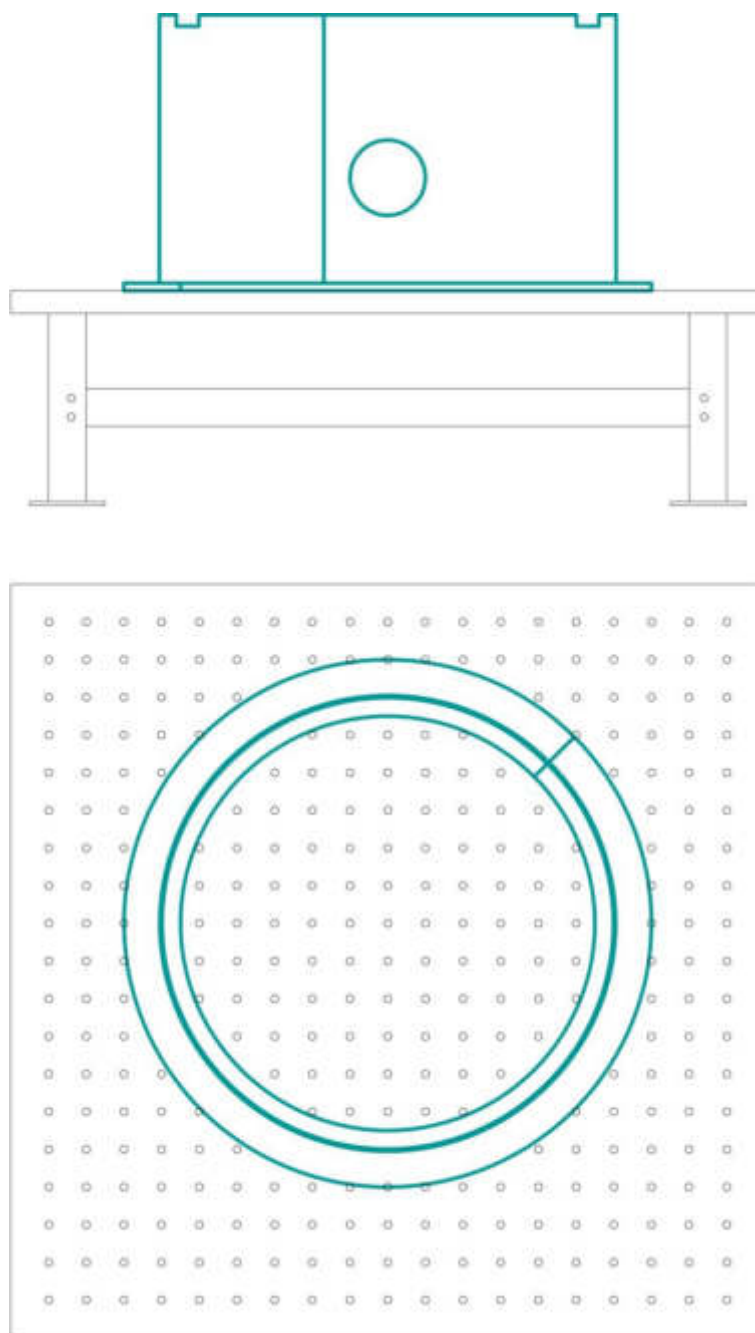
Схема сборки обечайки опорной и кольца опорного
